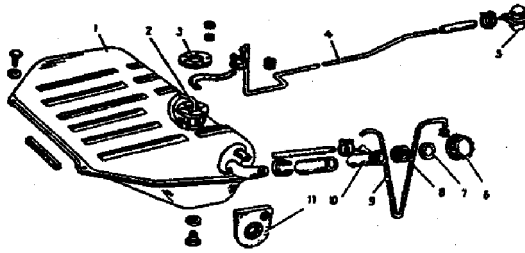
Conjunto do tanque de combustível e tubulações: 1 - tanque de combustível; 2 - bóia medidora do nível; 3 - junta; 4 - tubulação de combustível; 5 - bomba de combustível; 6 - tampa do tanque; 7 - junta; 8 - conexão do tubo de enchimento; 9 - tubo de respiro; 10 - tubo de enchimento; 11 - moldura dos tubos de enchimento e de respiro.
